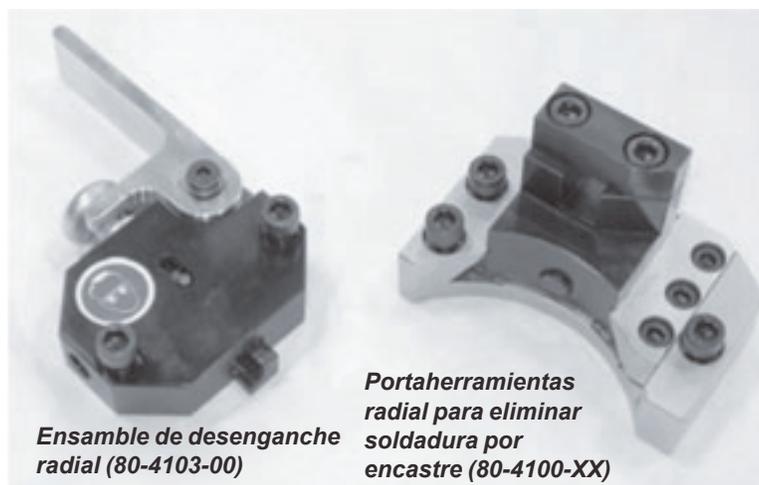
El portaherramientas radial para soldadura por encastre (80-4100-XX) utiliza un ensamble de desenganche radial estándar.
